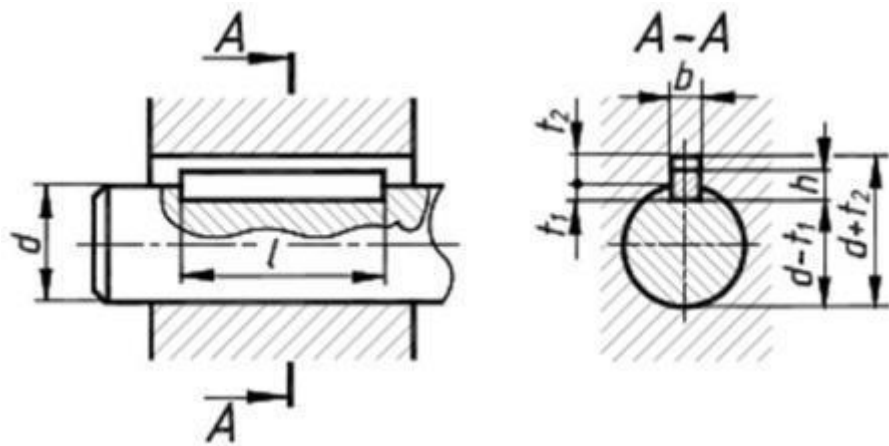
Чертеж соединения призматической шпонкой
